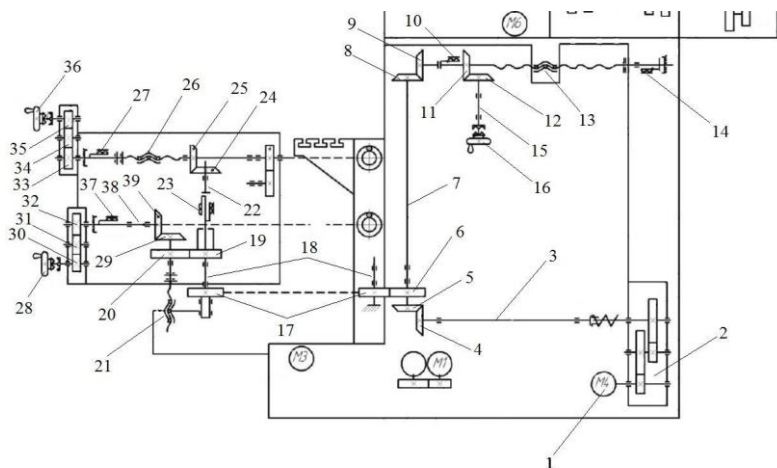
Кинематическая схема механизма подачи станка 6720ВФ2
